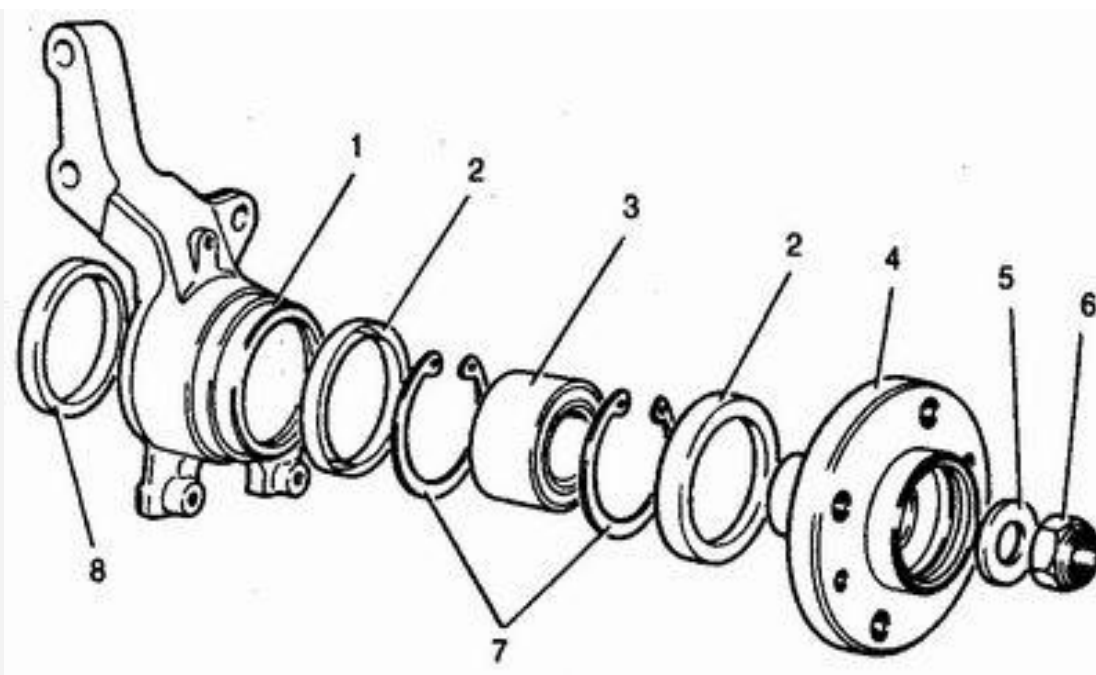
Поворотный кулак и детали ступицы переднего колеса.
